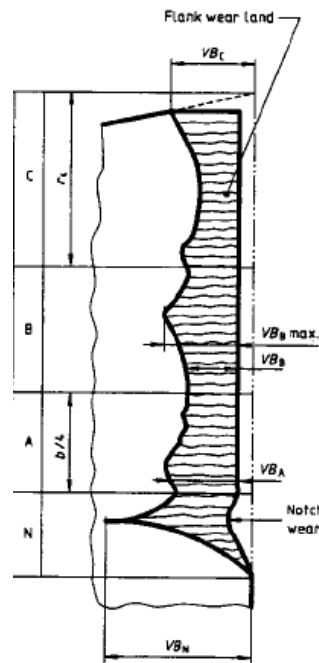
Zonas de desgaste del flanco de la herramienta [30]
